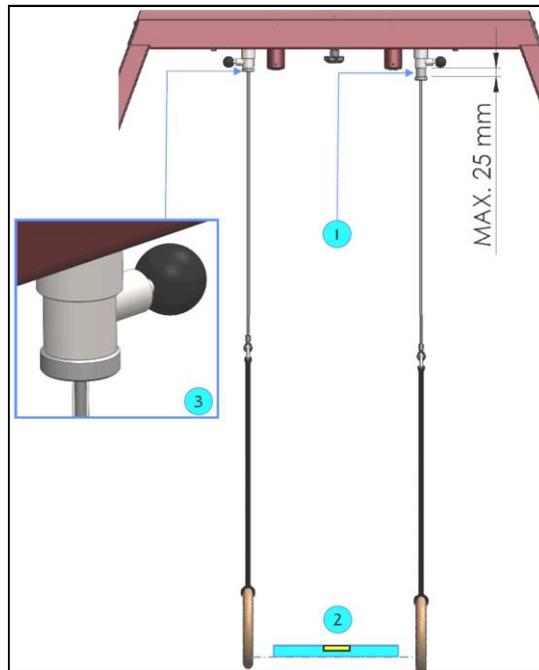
Detailansicht Gerüstrohre (oben)
